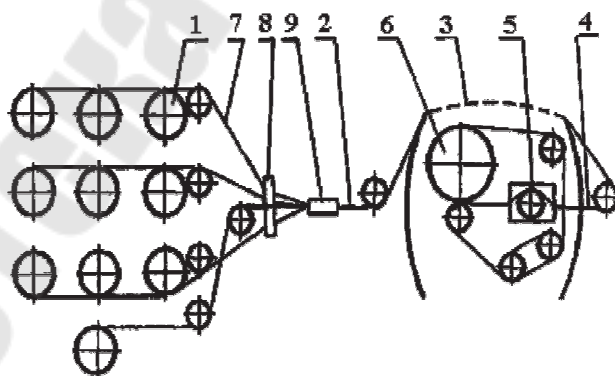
Кинематическая схема свивочной машины двойного кручения с внешним расположением питающих катушек («снаружи-вовнутрь»): 1 – питающая катушка; 2 – первичная свивка; 3 – «баллон»; 4 – вторичная свивка; 5 – торсионный узел; 6 – приемная катушка; 7 – проволока; 8 – распределительный шаблон; 9 – плашки
